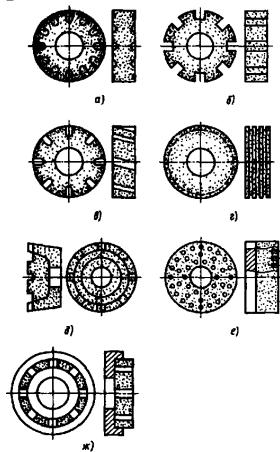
Круги с прерывистой рабочей поверхностью: а - выточками; б - прямыми пазами; в - наклонными пазами; г - кольцевыми канавками; д - пазами на торце; е - отверстиями; ж - сегментные
